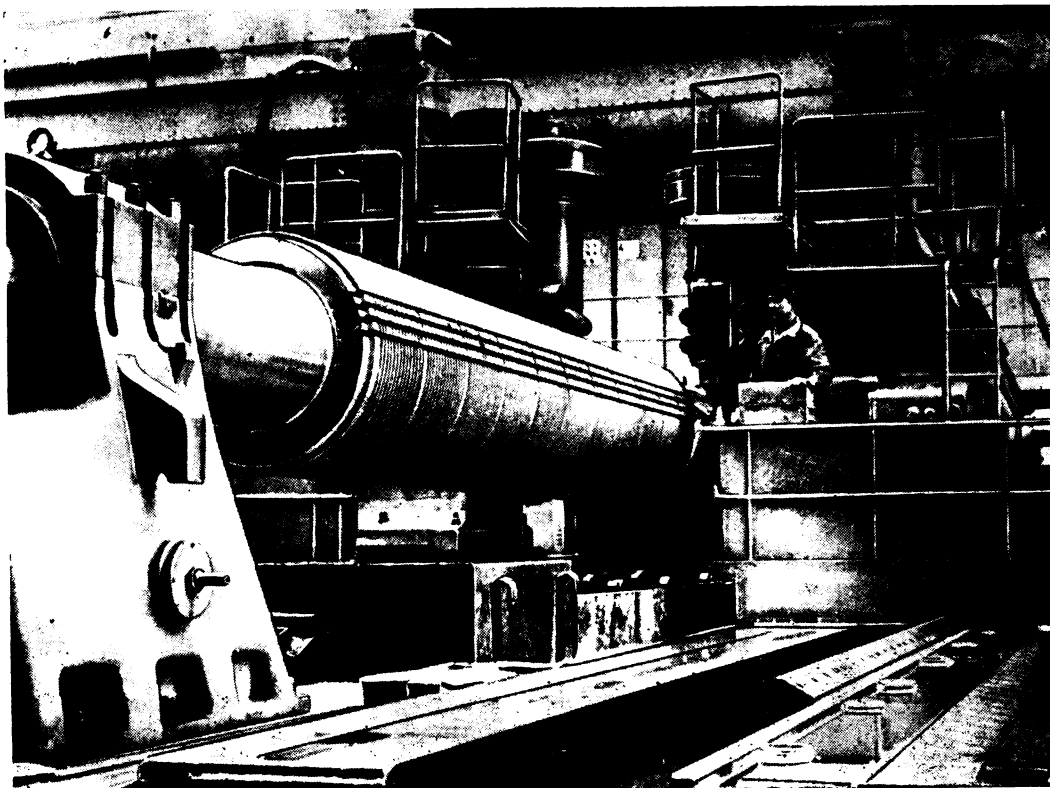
Фрезеровка пазов в роторе турбогенератора.
